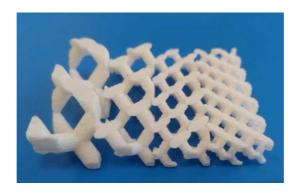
Pruebas de estructuras Diamond20 fabricadas en SLS
